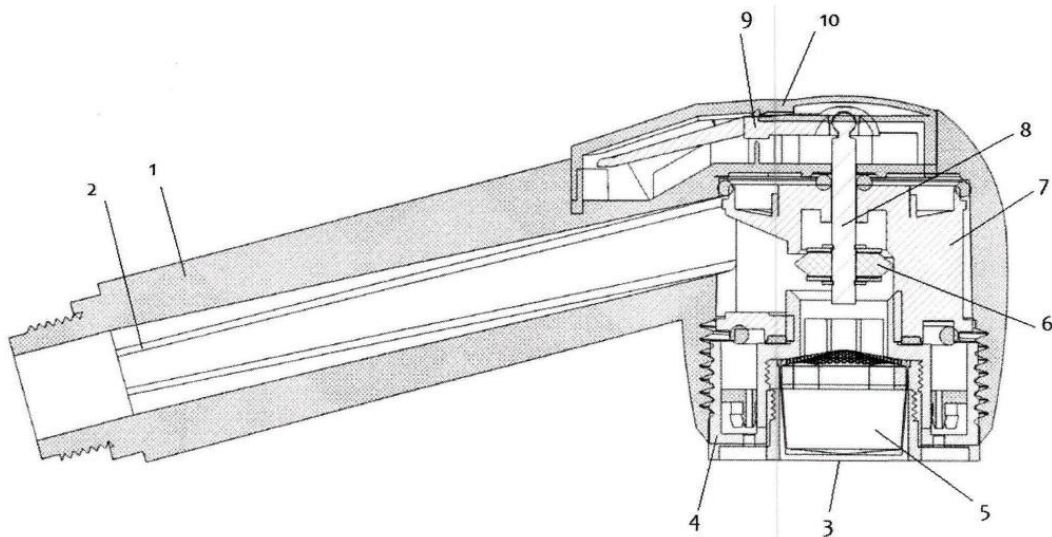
Душевая головка: 1 – корпус; 2 – подводящая трубка; 3, 4 – сетка; 5 – аэратор; 6 – клапан; 7 – диафрагма; 8 – шток; 9 – рычаг; 10 – крышка [56]
